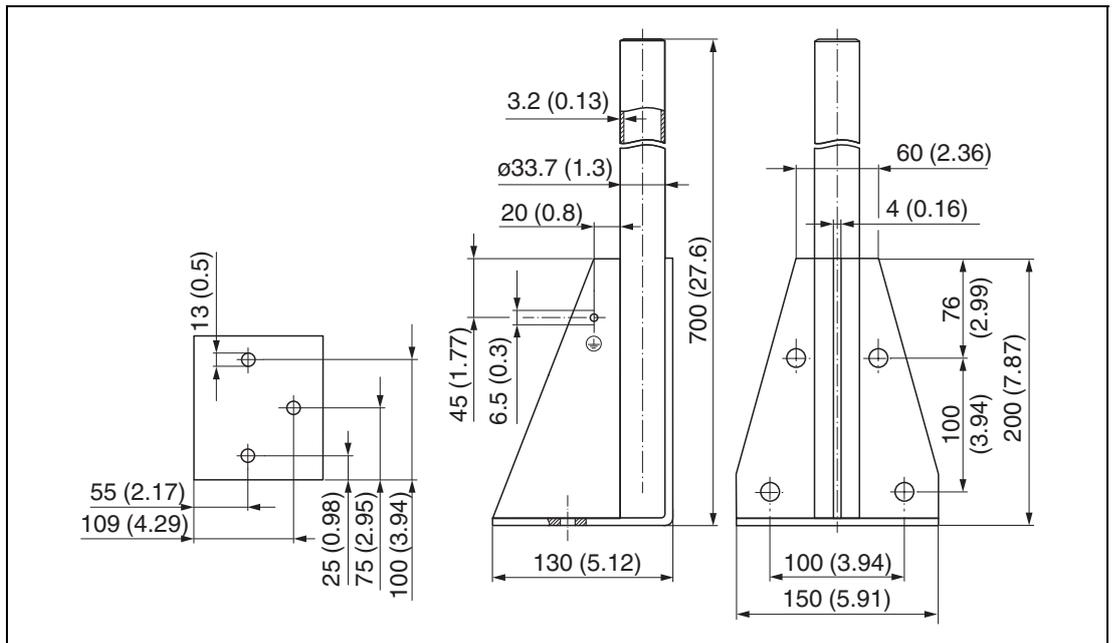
Abmessungen Montagegeständer (kurz), Maßeinheit: mm (Zoll)
